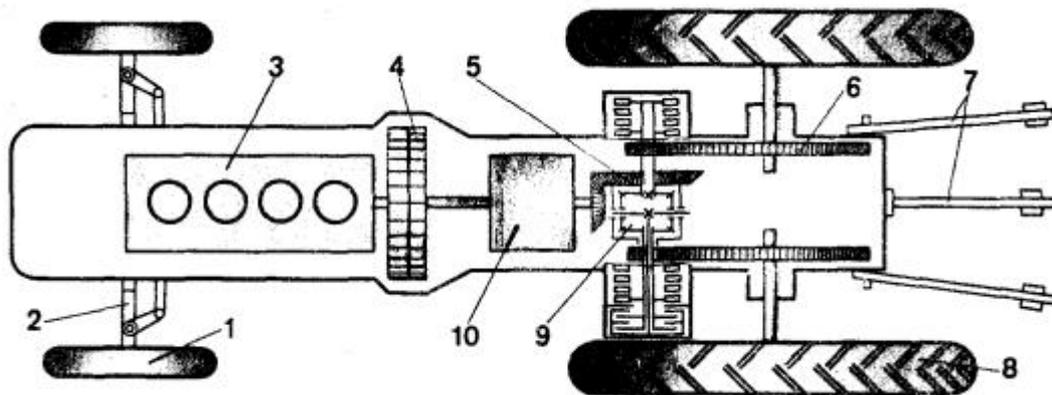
Расположение основных частей, их механизмов и деталей колёсного трактора МТЗ-80:
